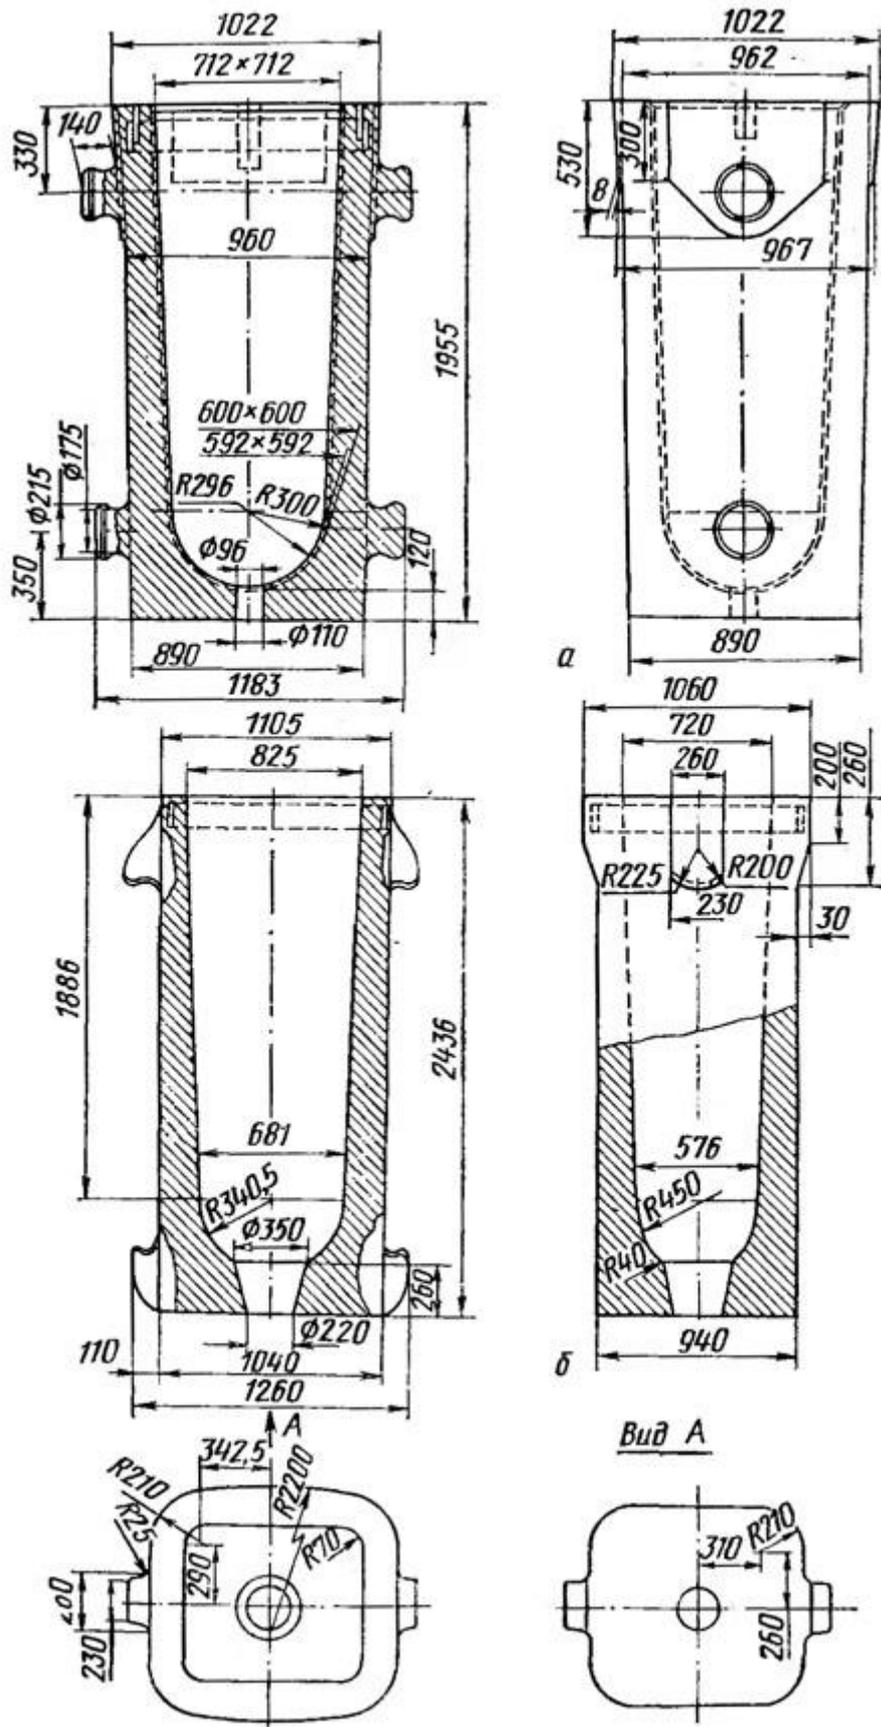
Изложницы с дном для разливки стали: а — сифоном; б — сверху
